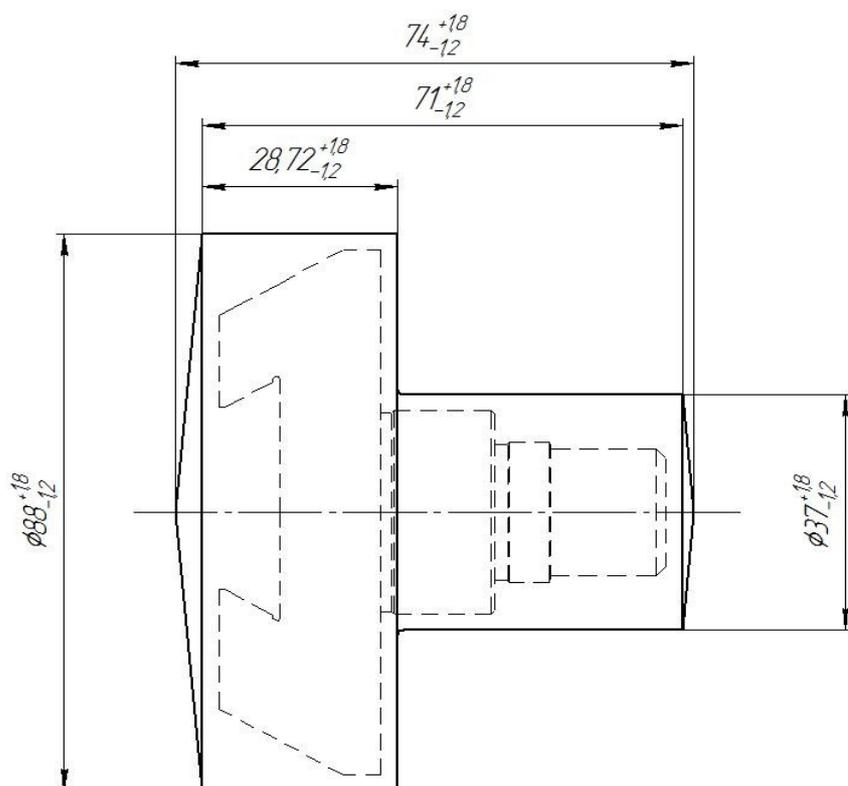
Эскиз заготовки сделанной методом штамповки
